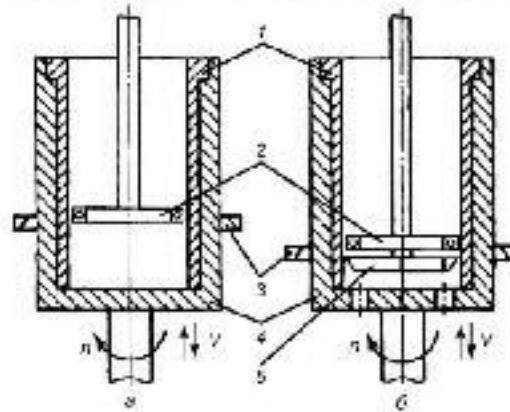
Схемы восстановления внутренней поверхности втулки в жесткой матрице а — незакаливаемых втулок; б — закаливаемых втулок; 1 — восстанавливаемая деталь; 2 — индуктор; 3 — устройство для охлаждения матрицы; 4 — матрица; 5 — устройство для охлаждения детали
